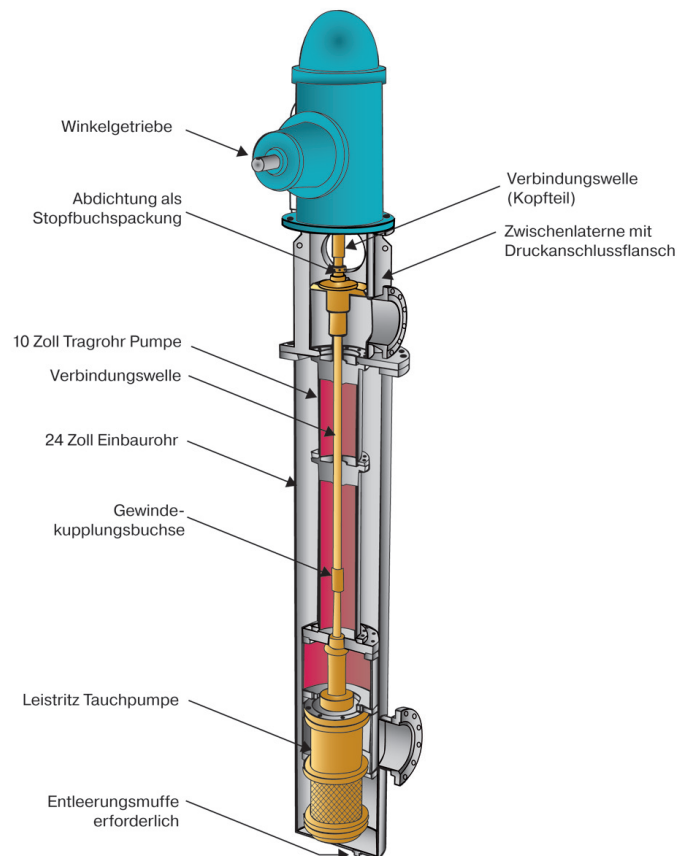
Schnittdarstellung Einbaurohr mit Pumpe
